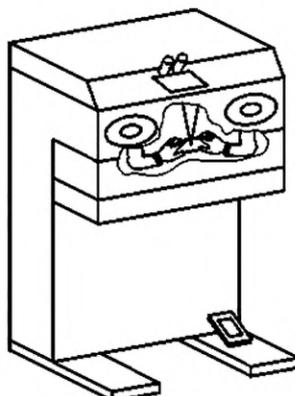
Стационарная ручная лазерная обрабатывающая машина (устройство), заготовка перемещается или позиционируется вручную
